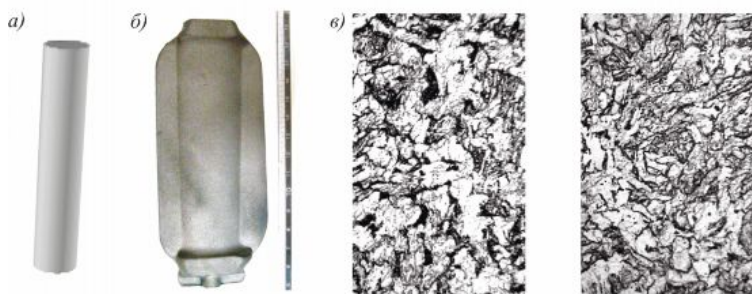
Общий вид исходной заготовки и штамповка лопатки – *a*;
